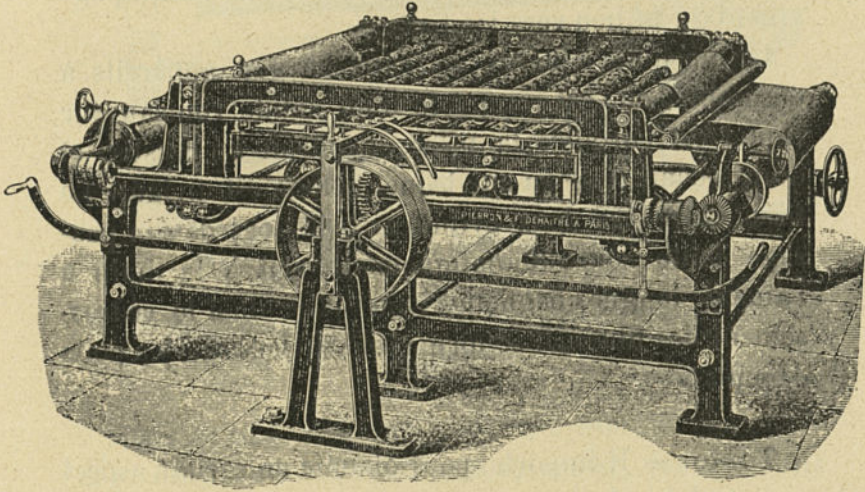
Machine à dérompre système Garnier (Dehattré).
